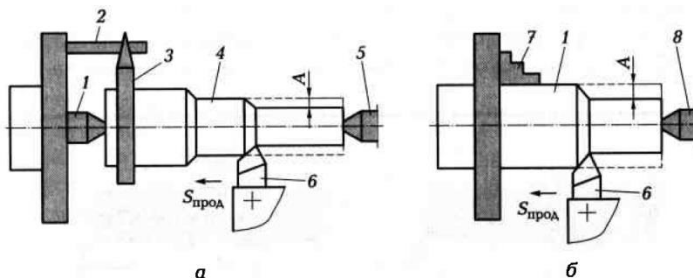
Схеми установки заготовки на токарному верстаті
